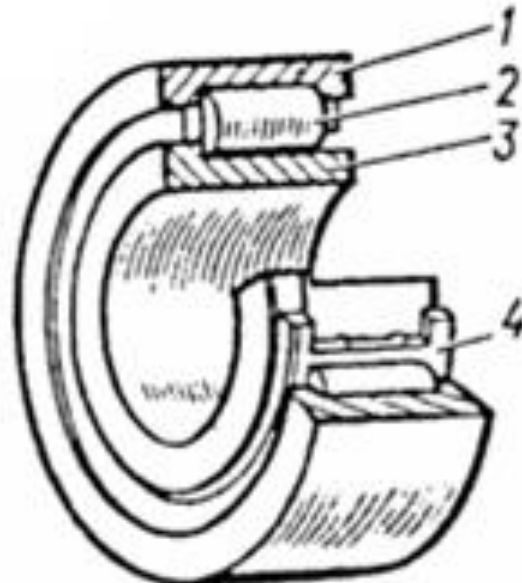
Циліндричний однорядний роликовий підшипник з одnobортним внутрішнім кільцем:
